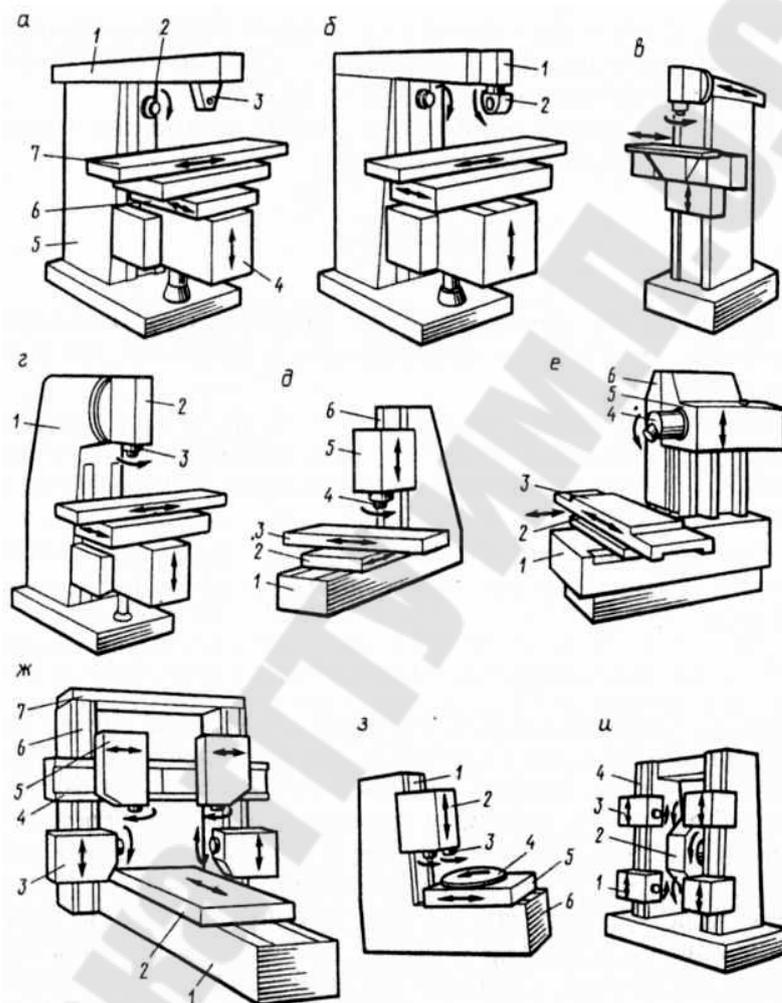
Разновидности фрезерных станков и движения на них
